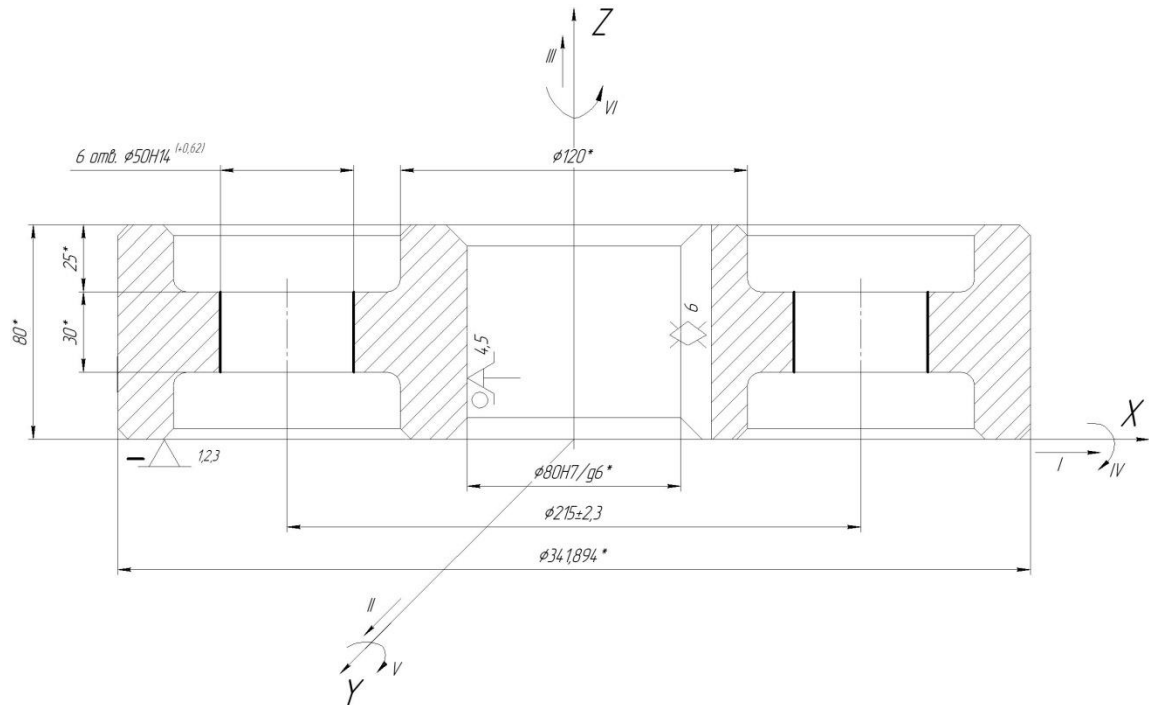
Схема базування заготовки на свердлильній з ЧПК операції
